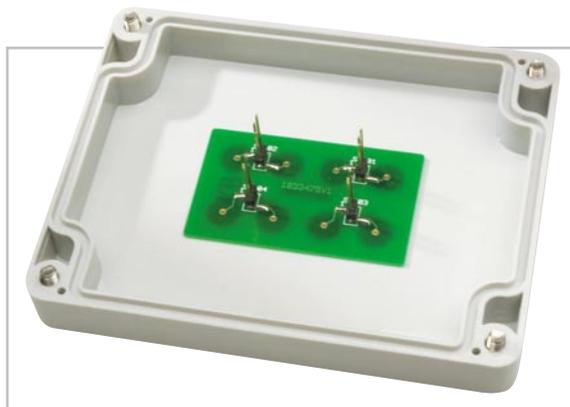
Tastenplatine, in IP-65-Gehäuse geklebt
